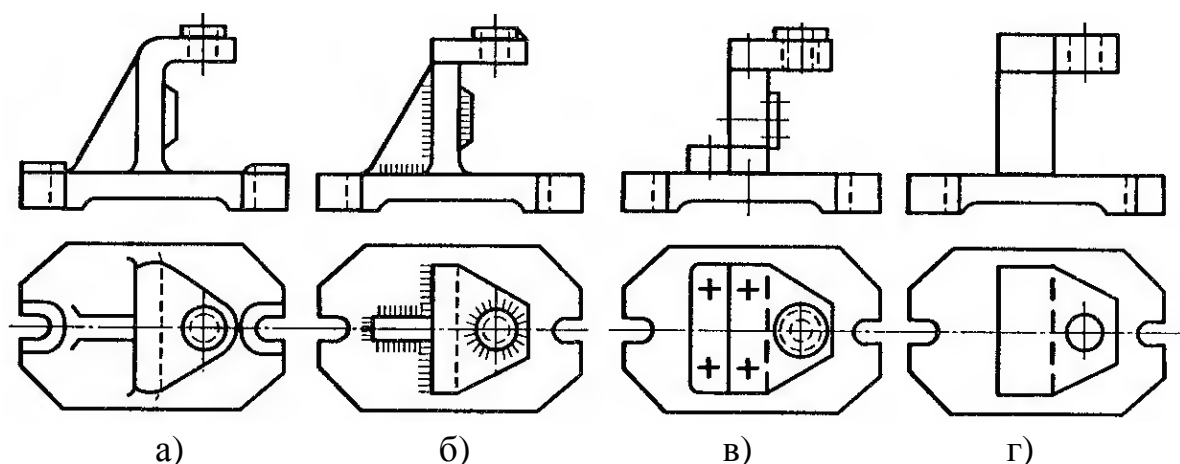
Варианты конструкции корпусов приспособлений:
